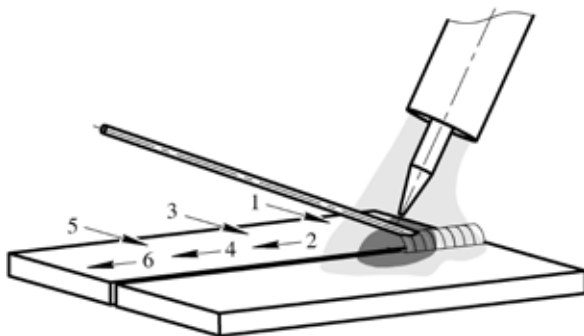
Пример манипуляции присадочной проволокой при TIG сварке.
